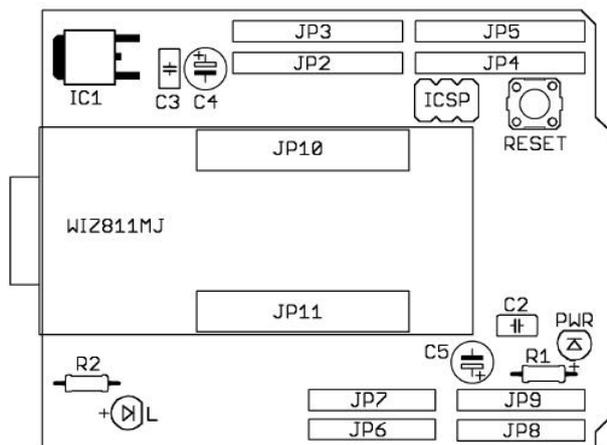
Схема сборки Freeduino E-Shield v1.21 Kit
